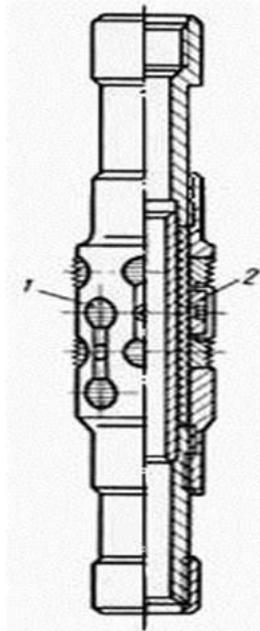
Гидравлический якорь (плашечный) 1 - плашки с насечками; 2 - резиновый цилиндр
